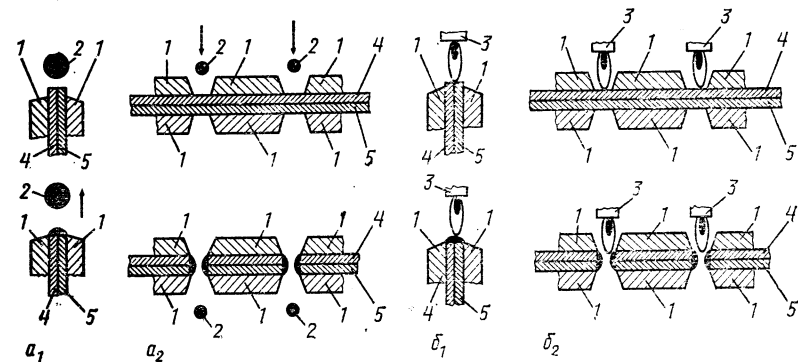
Принцип сварки: а — сварка нагретой проволокой (а<sub>1</sub> — сварка излучением; а<sub>2</sub> — резка/сварка); б — газопламенная сварка (б<sub>1</sub> — сварка; б<sub>2</sub> — резка/сварка); 1 — зажимные планки; 2 — нагретая проволока; 3 — водородно-кислородное пламя; 4, 5 — свариваемые детали
